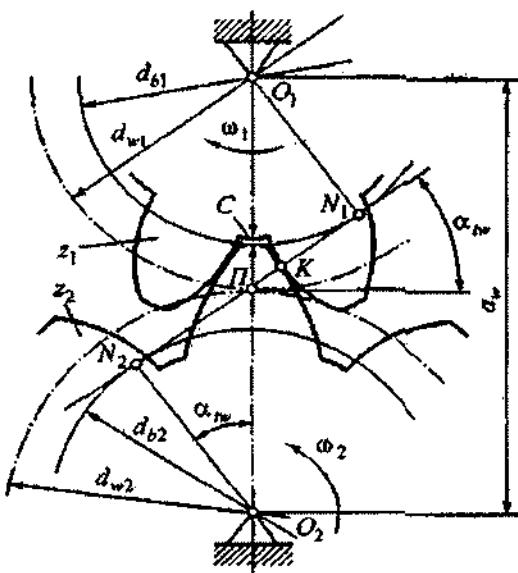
Зацепление эвольвентных зубчатых колес
